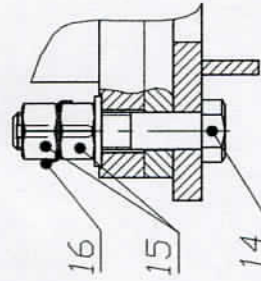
Опора редуктора ЕЮК-160-1М и ВБА-32/2
